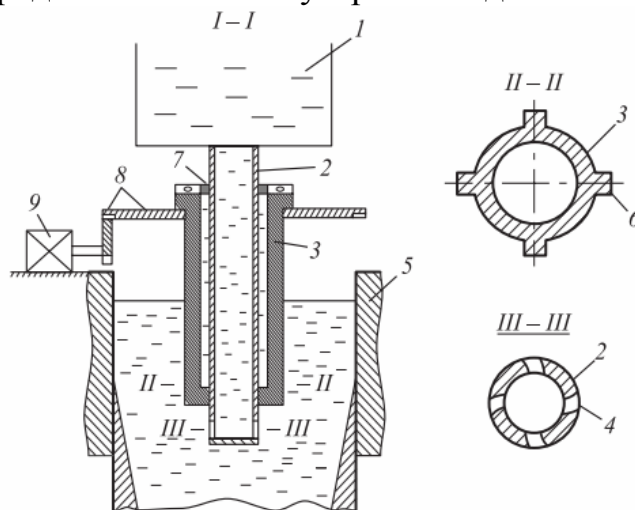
Схема устройства для подачи и перемешивания стали в кристаллизаторе с вращающейся рубашкой с вертикальными ребрами
